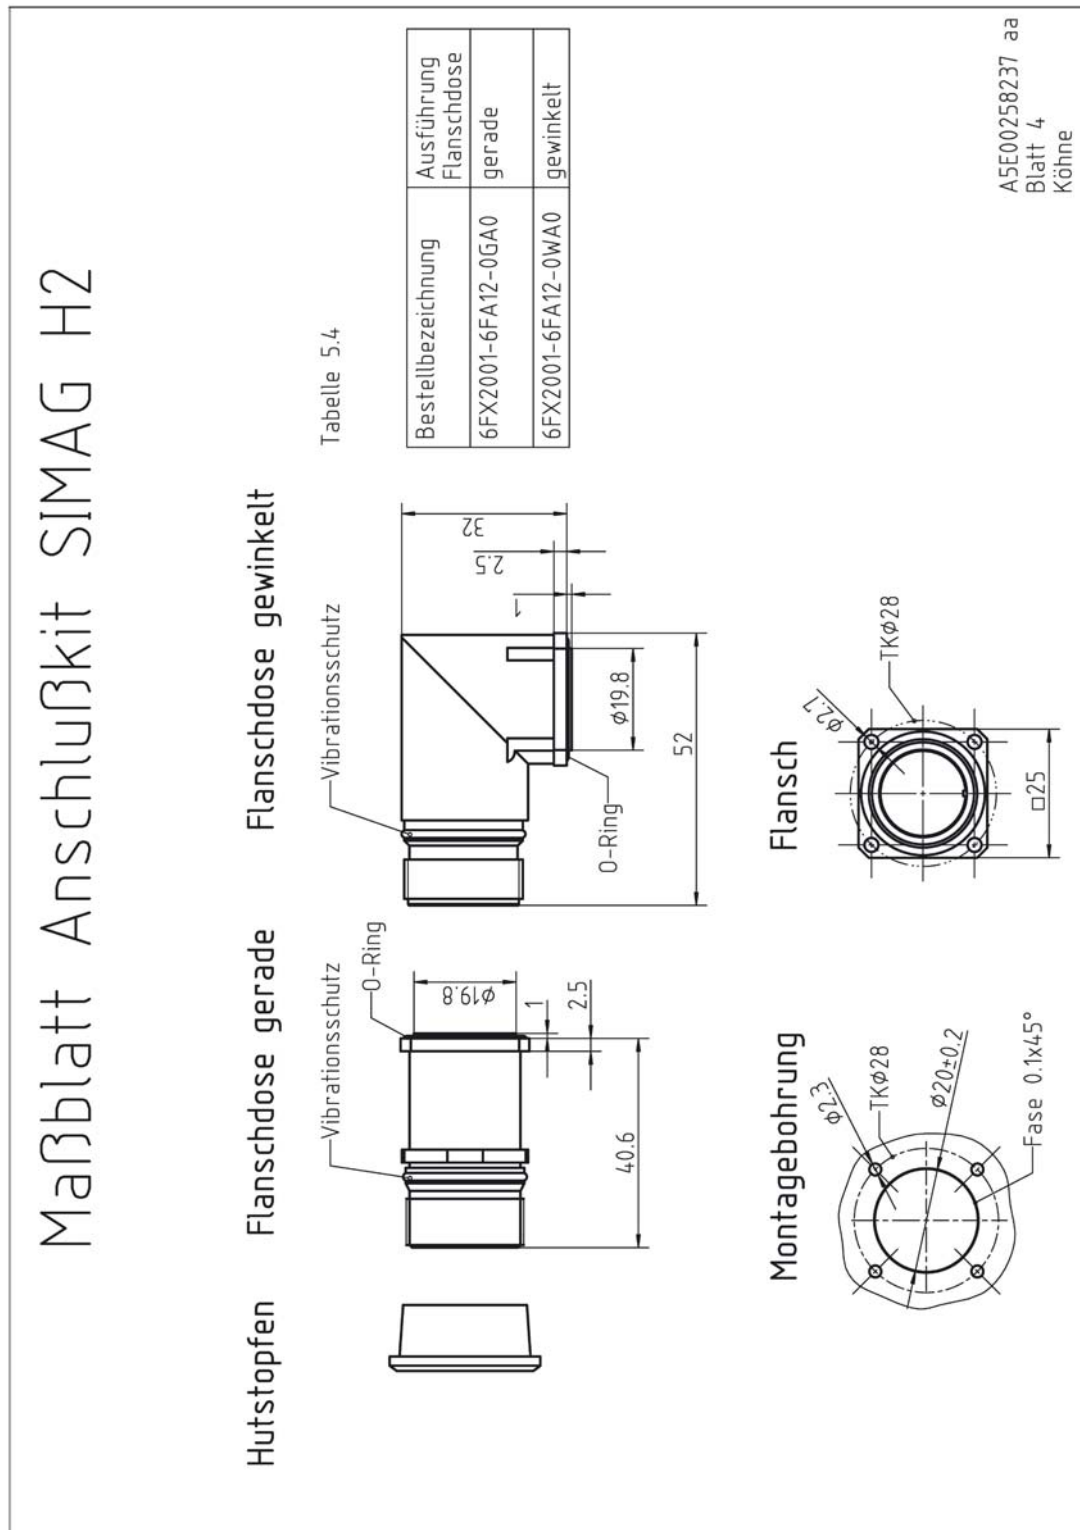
Габаритный чертеж комплекта для подключения SIMAG H2
